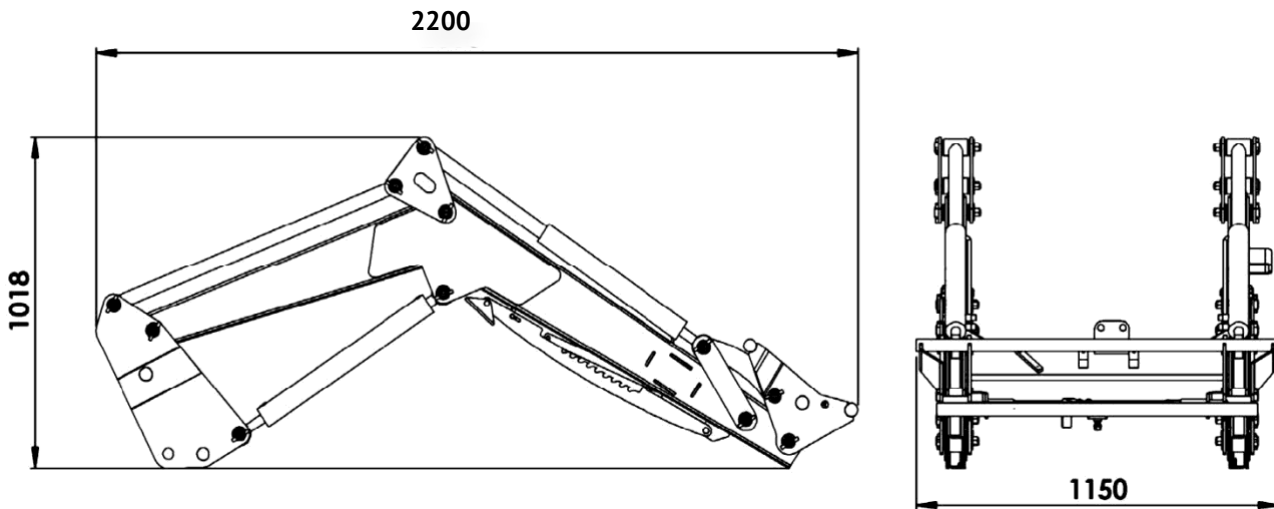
Примерные размеры погрузчика подготовленного для транспортировки
